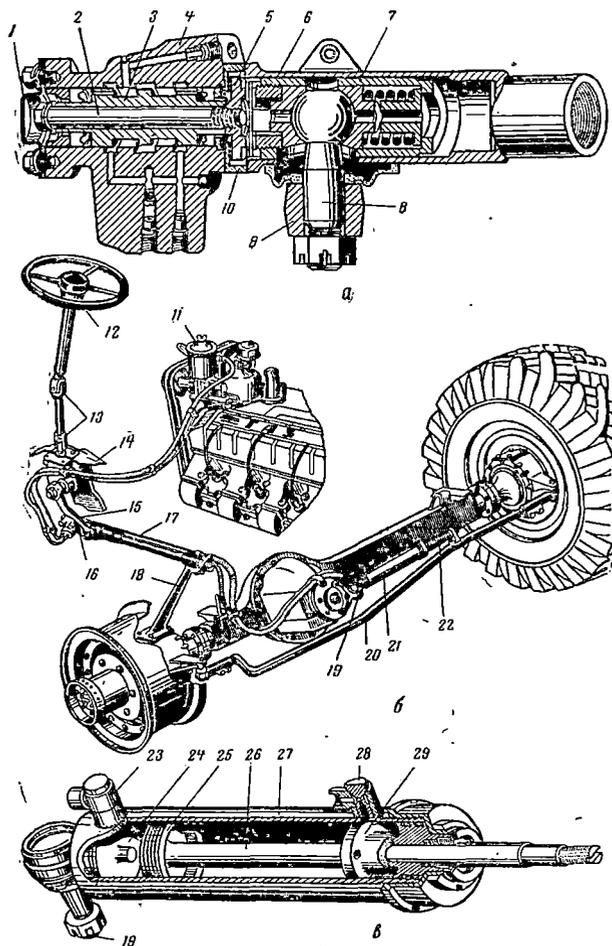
Рулевой привод автомобиля ГАЗ-66:
